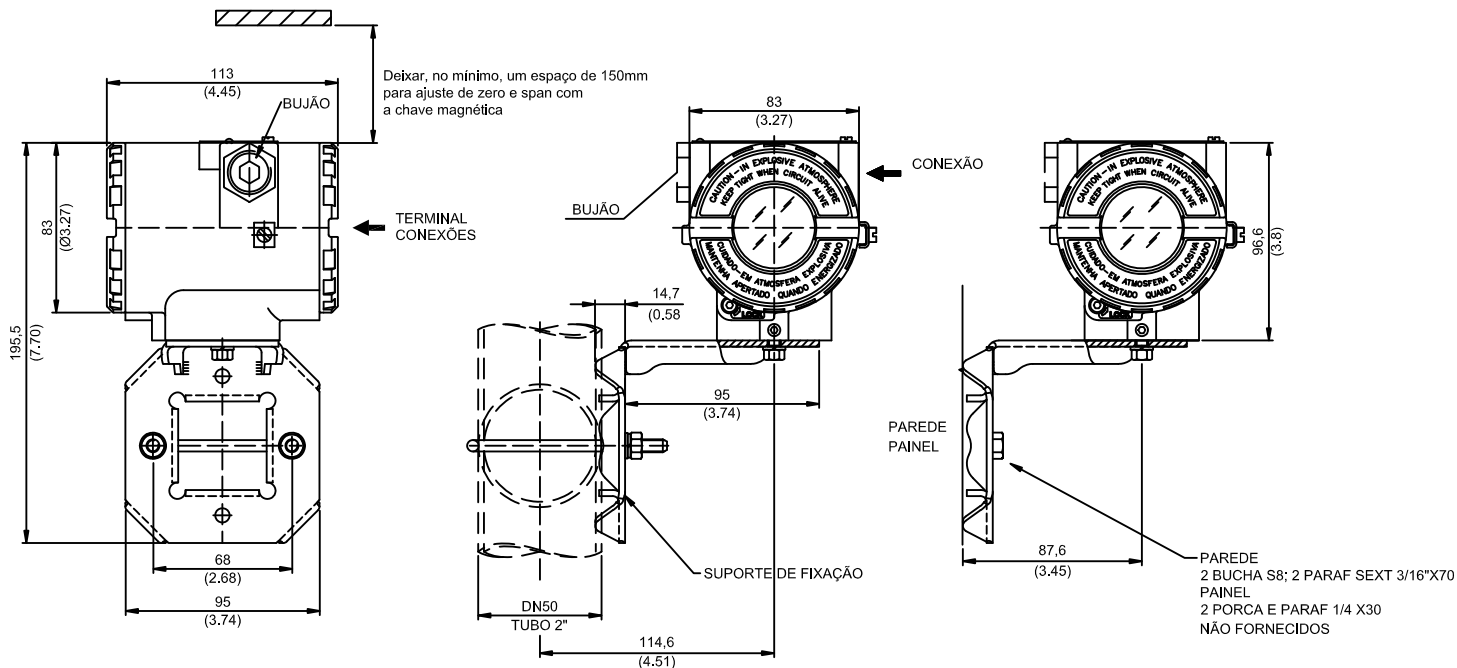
Desenho Dimensional e Posições de Montagem
